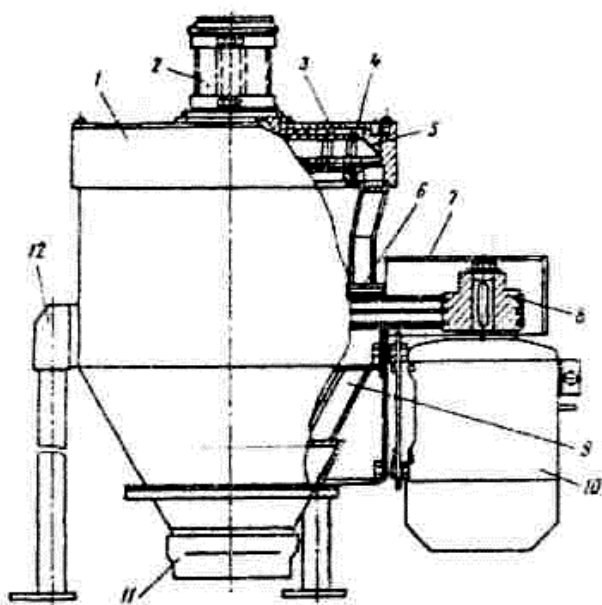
Энтолейтор РЗ-БЭЗ:1 - корпус; 2— приемный патрубок; 3 — диск; 4 — втулка; 5 — отражательное кольцо; 6,7 — кожухи; 8 — шкив; 9 — полость; 10 — электродвигатель; 11 — выпускной патрубок; 12- стойка.
